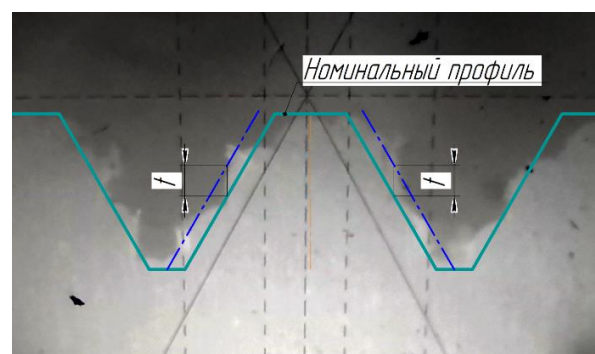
Профиль резьбы M8, сформированной в образце из PETG-пластика
